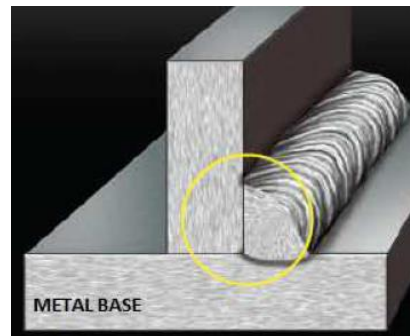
Fusión incompleta cordón de soldadura [4].
